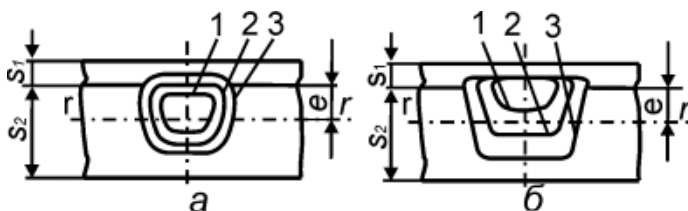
Кінетика формування ядра в деталях різної товщини ($r-r$ – поверхня теплової рівноваги; e – відстань цієї поверхні від зварюваного контакту); a – м'який, b – жорсткий режими зварювання; 1–3 – ізотерми плавлення на початку, посередині та наприкінці зварювання
